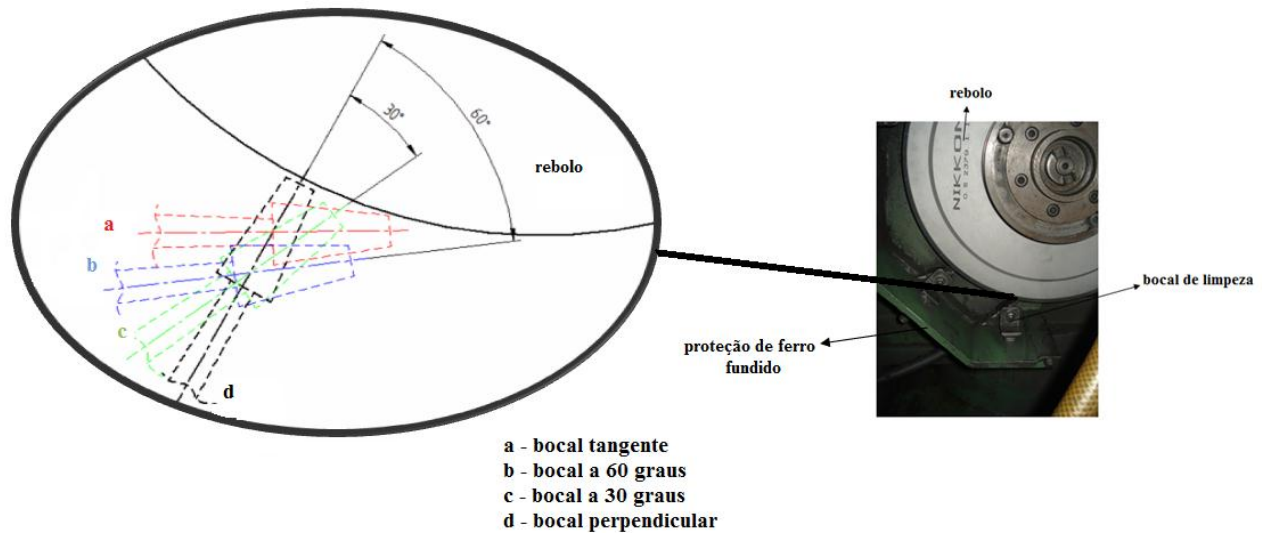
Desenho esquemático das orientações do bocal de limpeza.
